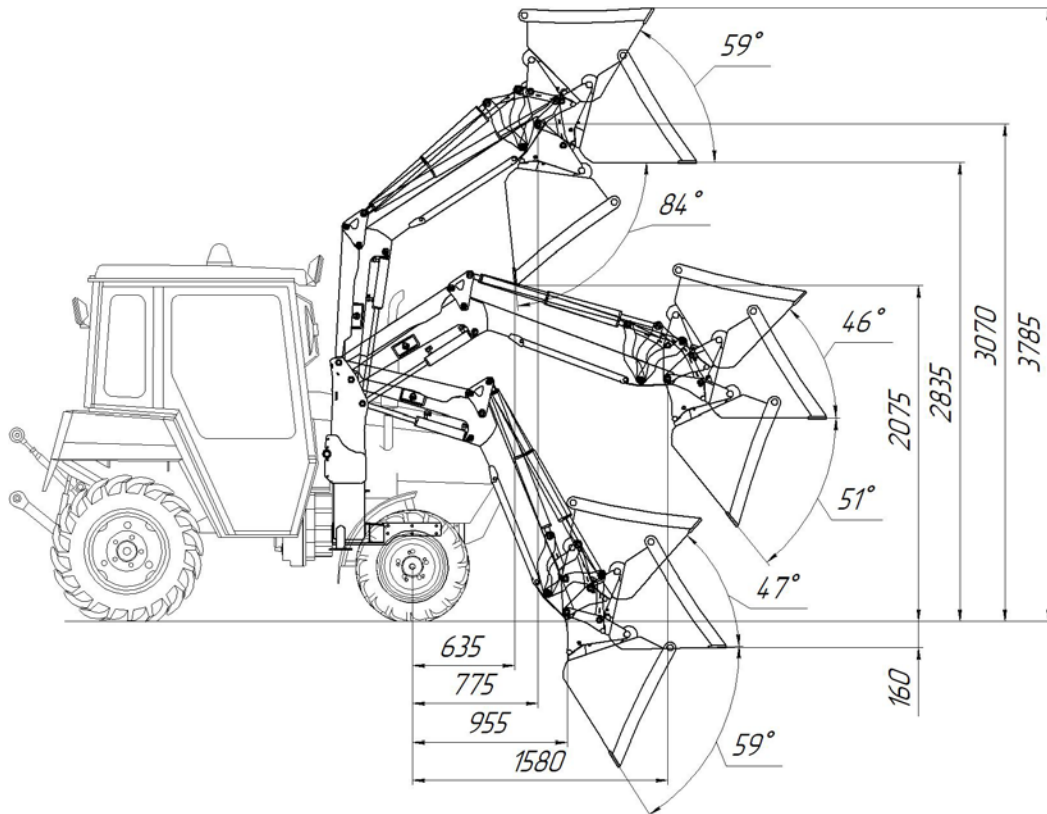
Габаритные размеры погрузчика Универсал 400
